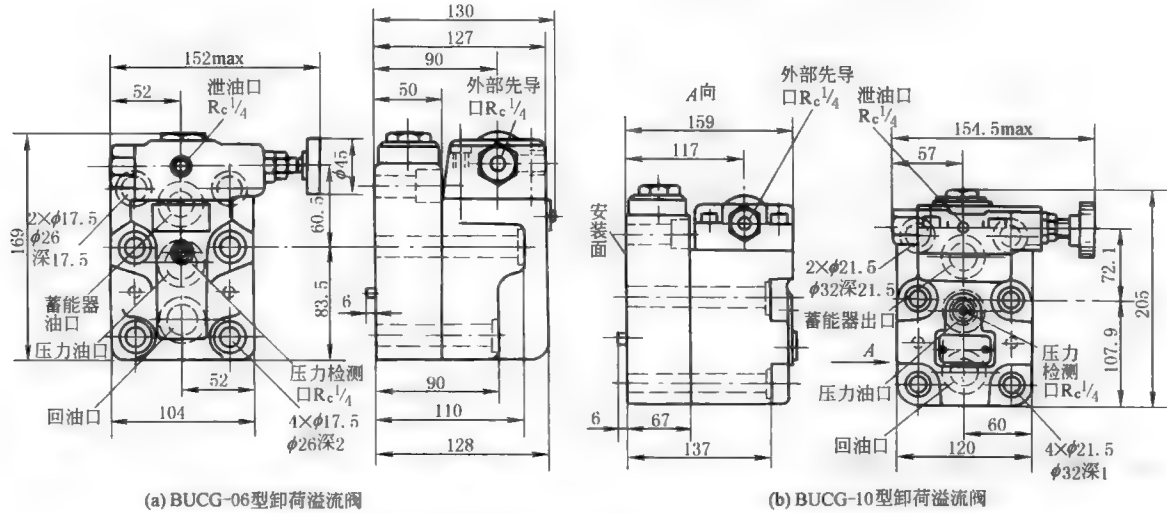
BUC 型卸荷溢流阀外形尺寸
